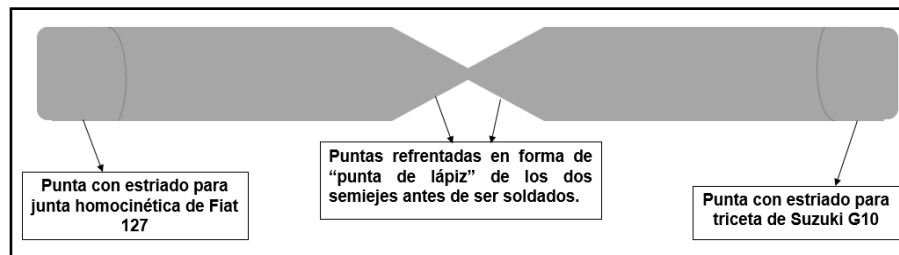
Ejes Cortados Y Torneados Antes De Ser Soldados
